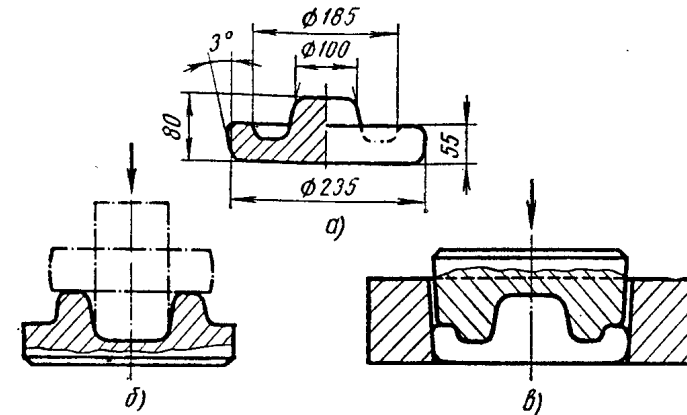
Схема машиннойковки полумуфты: а — эскиз поковки, б — осадка заготовки, в — формовка
